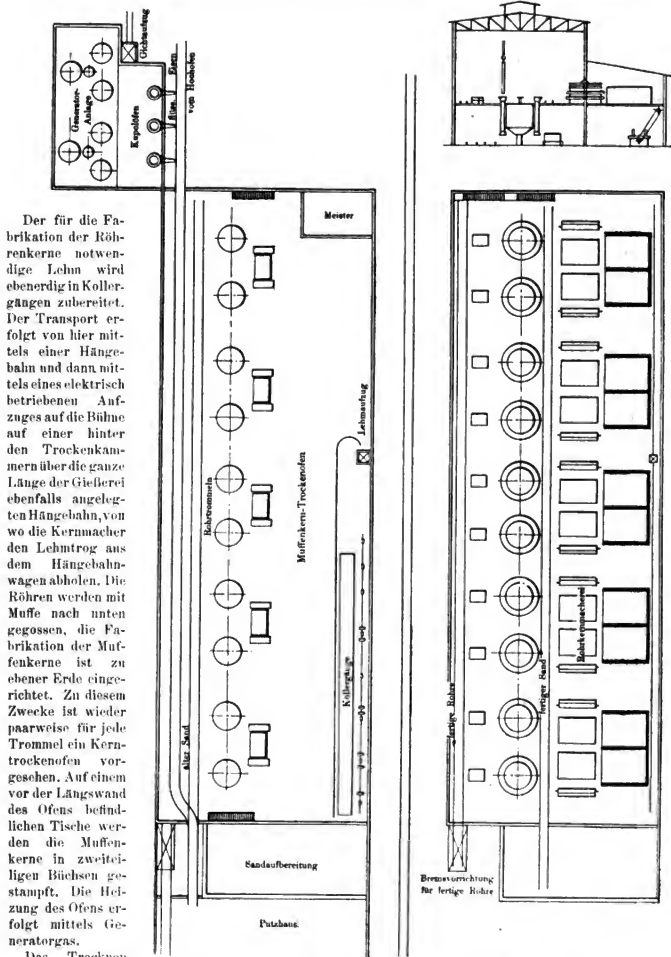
Lageplan einer Röhrengießerei mit 10 Blechtrommeln.
